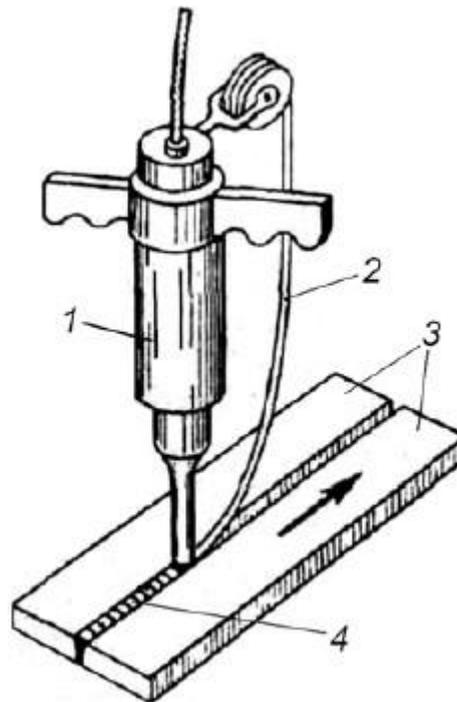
Схема ультразвуковой сварки с присадочным материалом: 1 – преобразователь с волноводом; 2 – присадочный материал; 3 – свариваемые детали; 4 – сварной шов.
